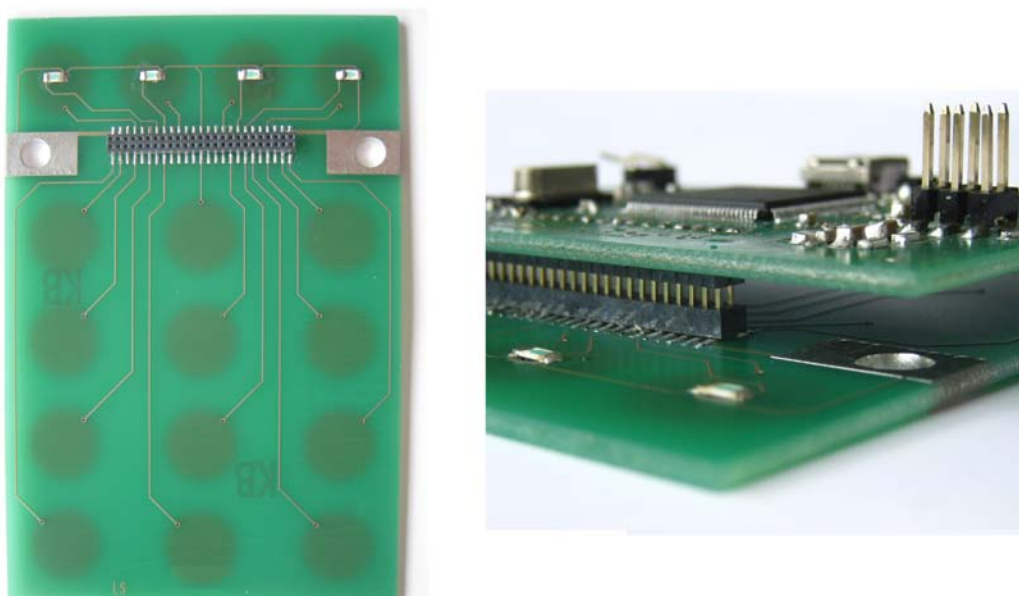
Scheda pad touch, con piste equidistanti, pad per metal cap e led reverse mounted.
